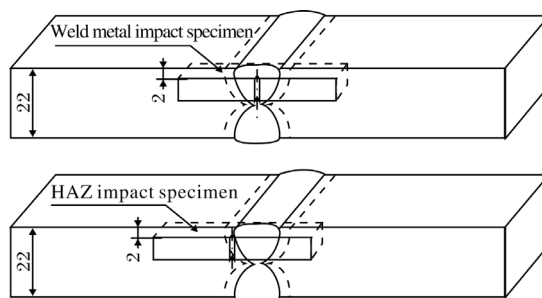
A-TIG 焊接试板焊缝及 HAZ 冲击试样取样示意图
